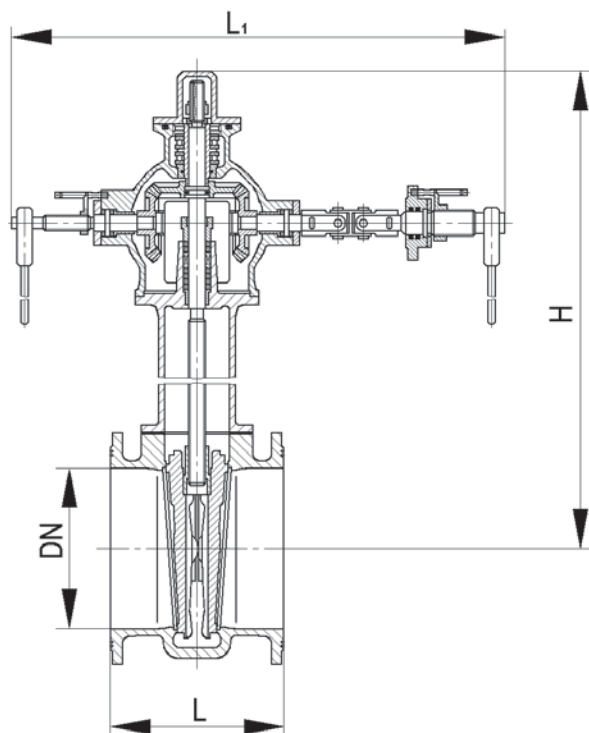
Задвижка клинкетная фланцевая с ручным приводом
